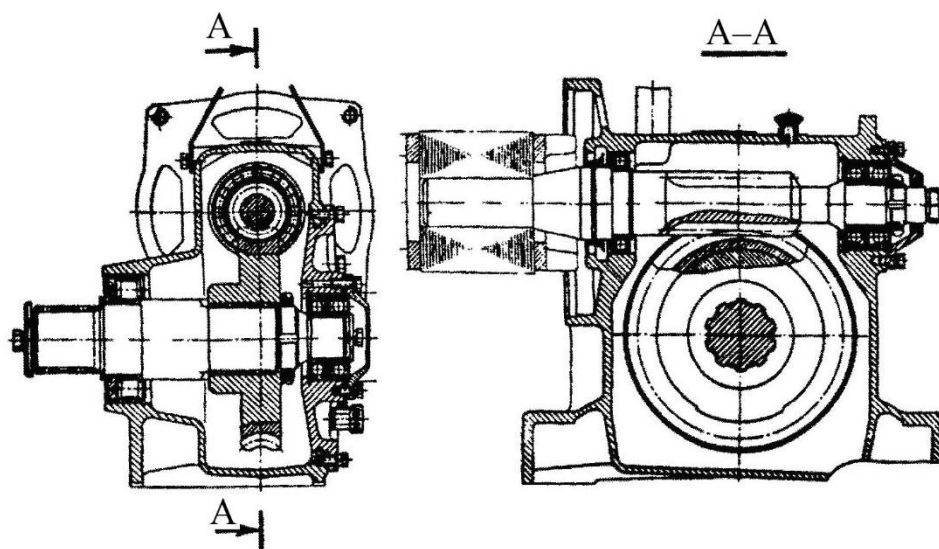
Редуктор с верхним расположением цилиндрического червяка
